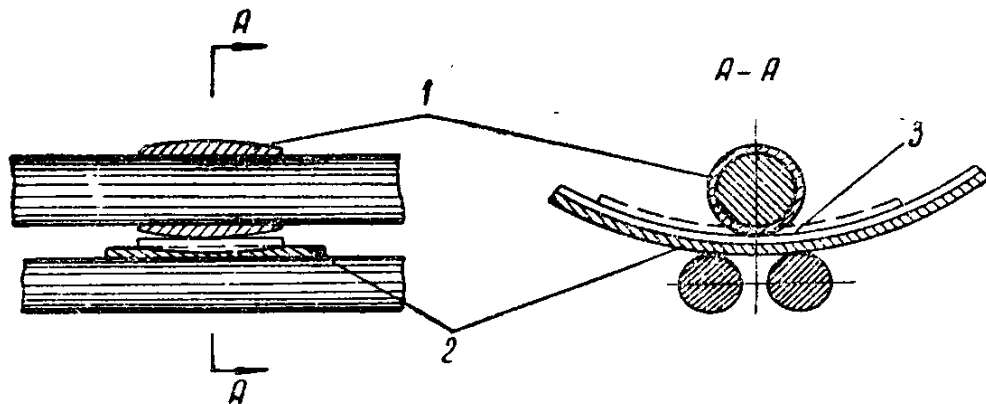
Приспособление к листогибочным вальцам для гибки листовых деталей по сферической поверхности: 1 — бочка; 2 — постель; 3 — изгибаемая деталь.
